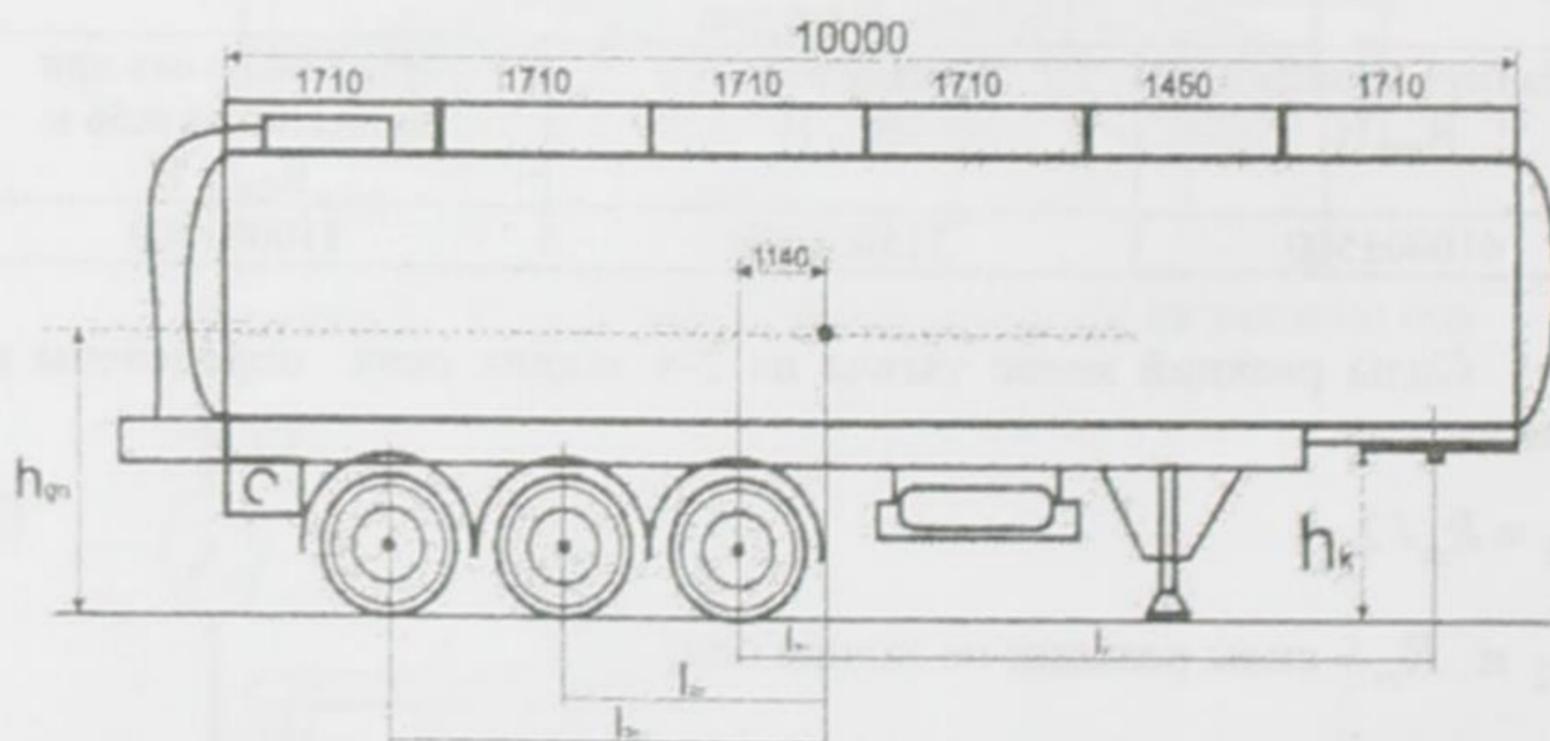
Габаритные размеры полуприцепа ФРЮЕХАУФ-
